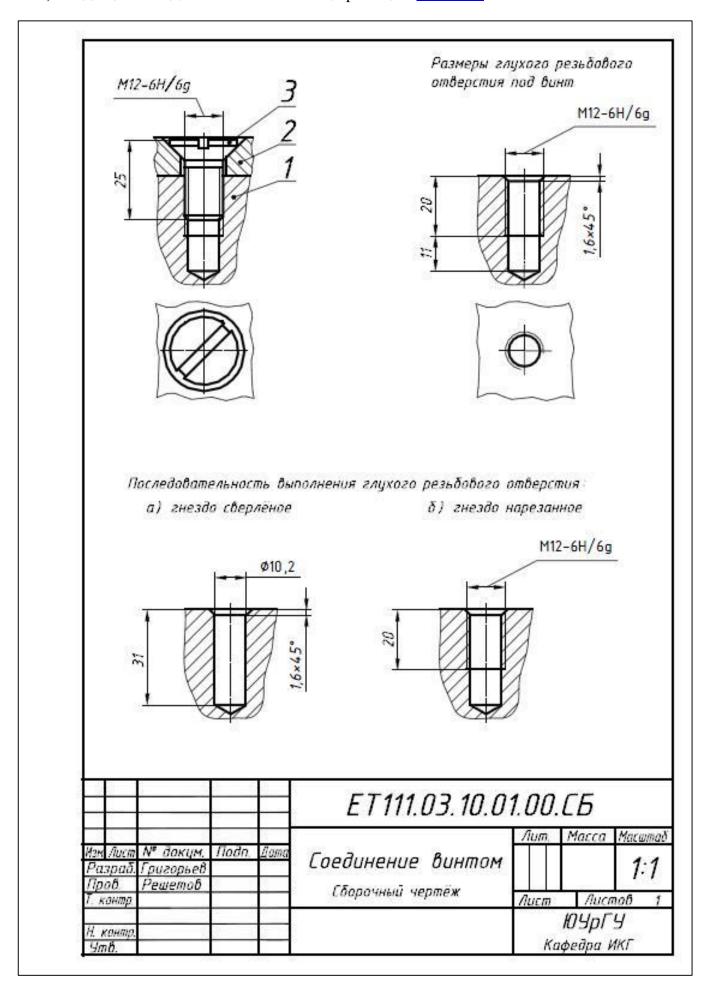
Пример выполнения сборочного чертежа «Соединение винтом»
